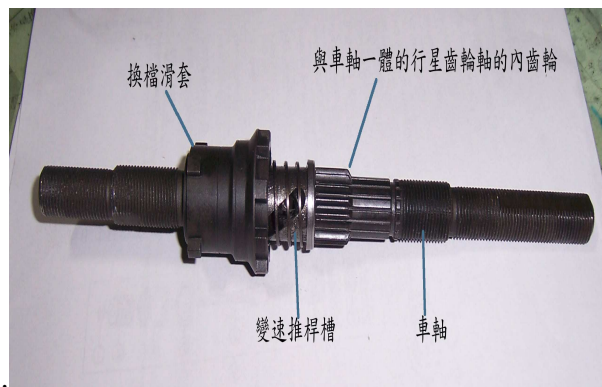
零件編號 6- AXLE UNIT 車軸細部說明圖示
